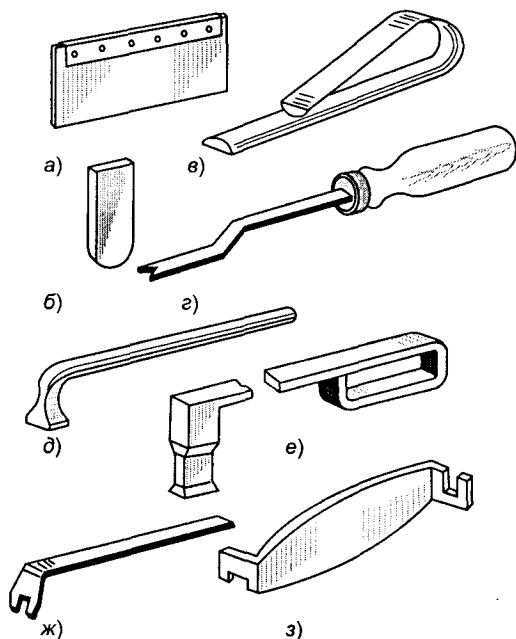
Набор инструмента обмотчика: а — фибровая пластинка; б — фибровый язык; в — обратный клин; г — угловой нож; д — выколотка; е — топорик; ж и з — ключи для гибки роторных стержней
